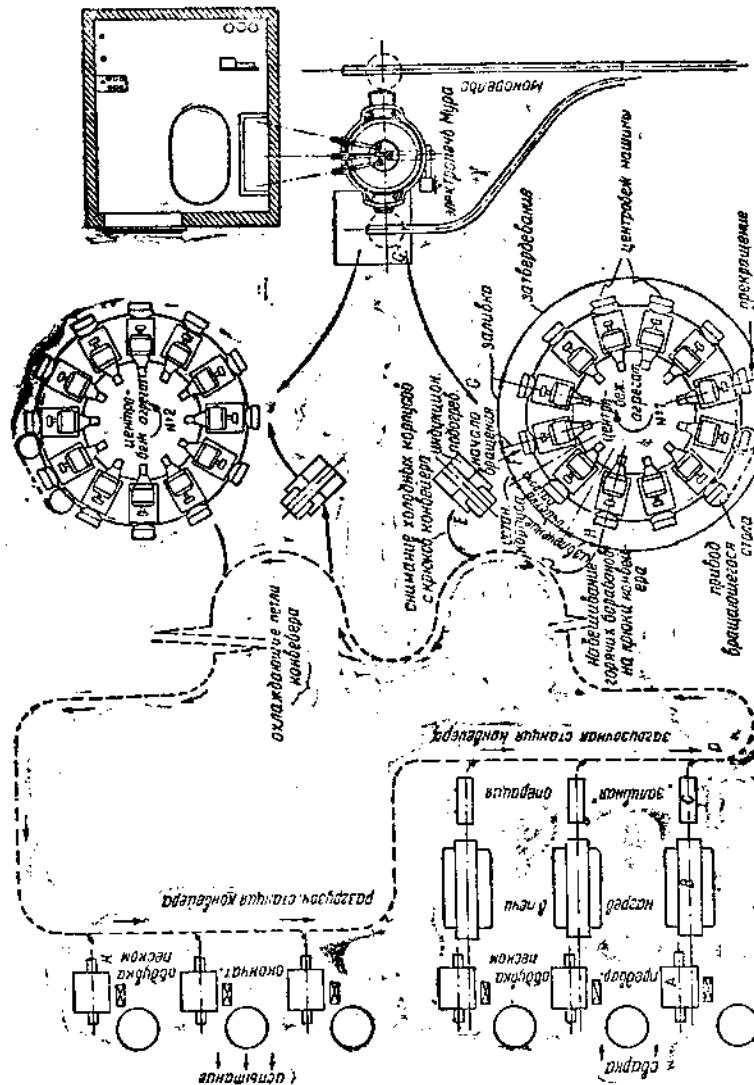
Схема цеха для выплавки чугуна в барабанах.
